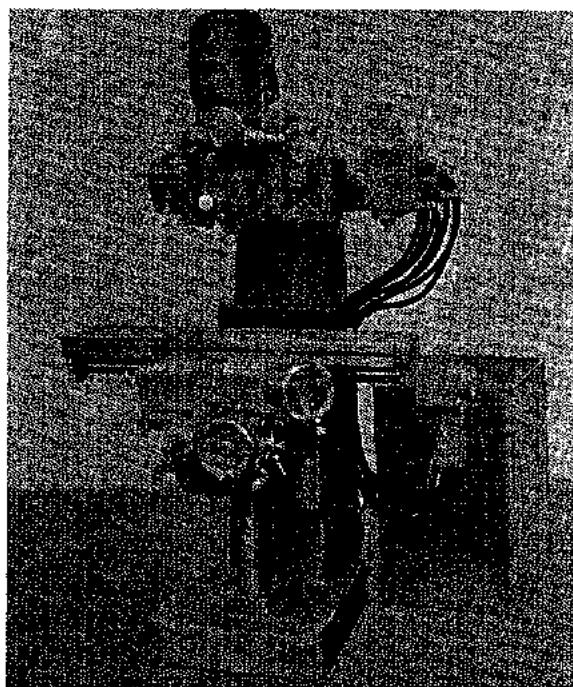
Fresadora para útiles y matrices (Cincinnati Milling Machine Co.)
